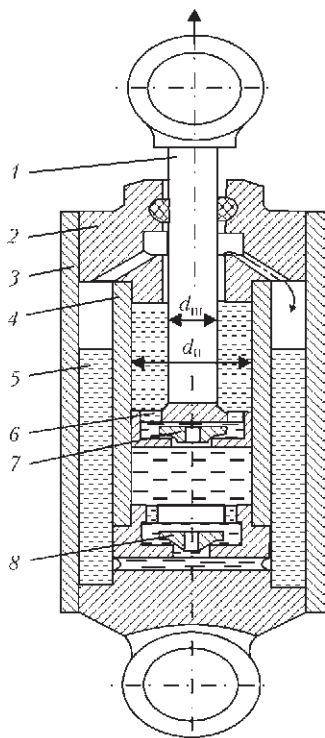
Конструктивная схема гидравлического гасителя колебаний: 1 – шток; 2 – направляющая втулка; 3 – корпус; 4 – рабочий цилиндр; 5 – резервуар; 6 – поршень; 7 – верхний клапан; 8 – нижний клапан
